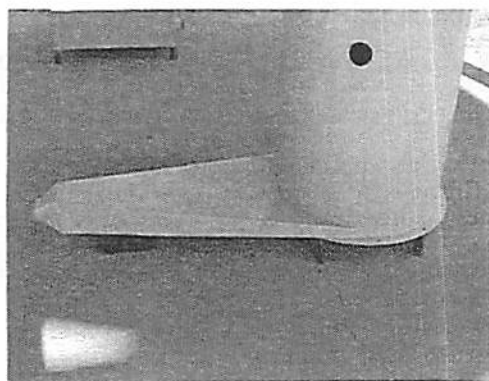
Detalhe da área de expansão soldada ao cilindro
